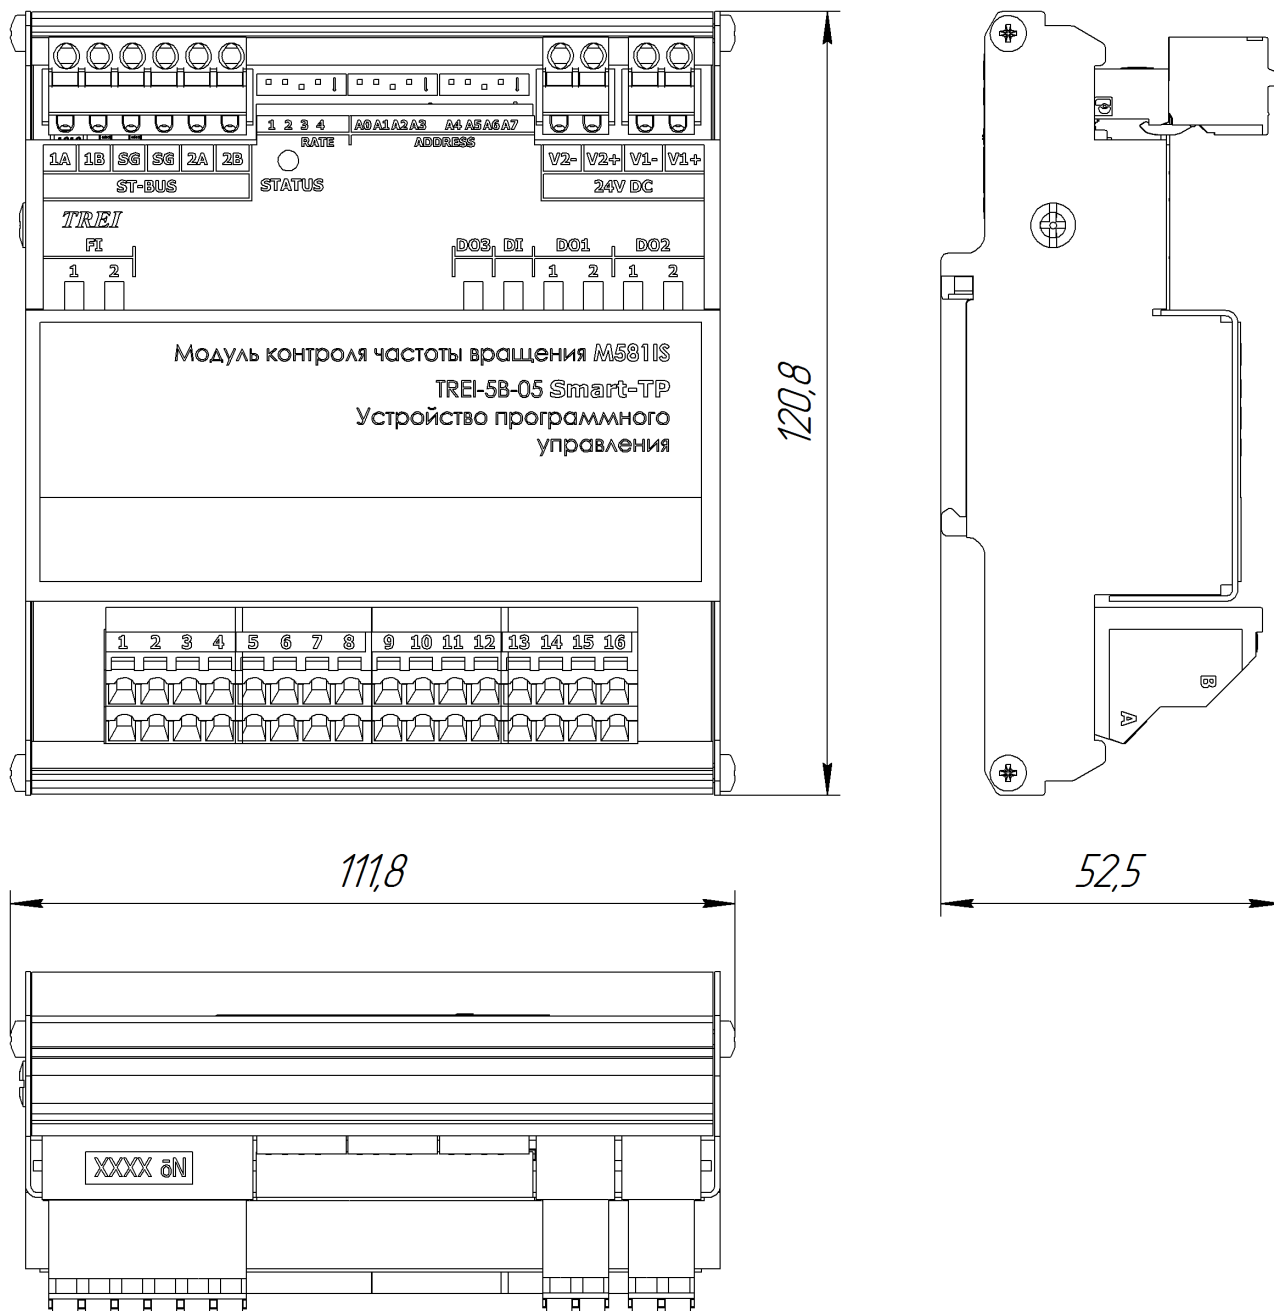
Чертеж общего вида M581IS с указанием габаритных и присоединительных размеров
